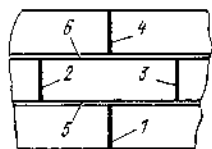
Последовательность сборочно-сварочных операций
